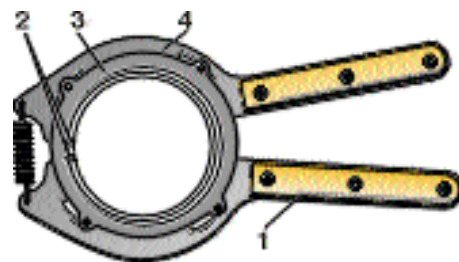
Приспособление для снятия и установки поршневых колец: 1 – рукоятка; 2 – выступы; 3 – упоры; 4 – захваты
